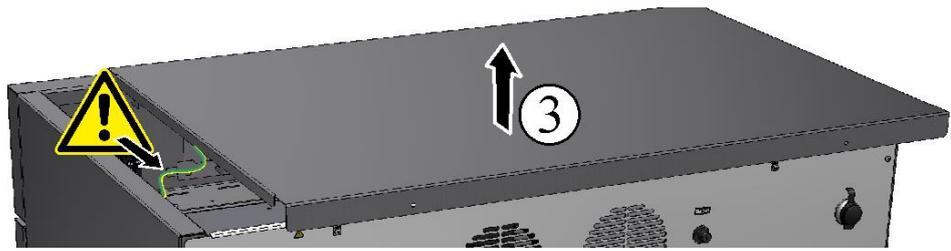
Soulever et déposer le couvercle (figure analogue)
